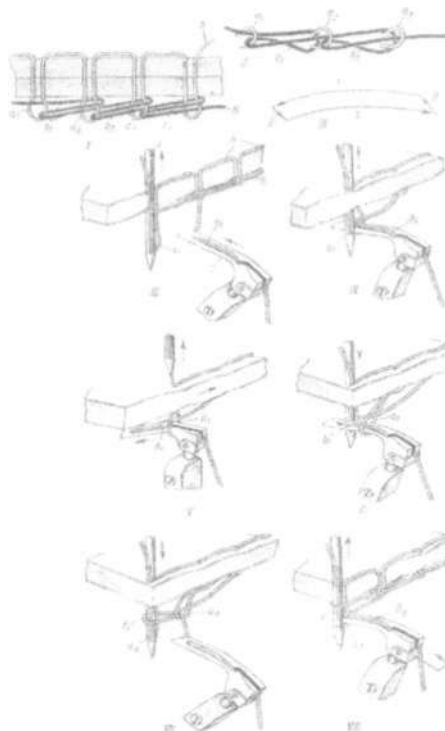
Процесс образования двухниточного цепного стежка и схемы строчек
